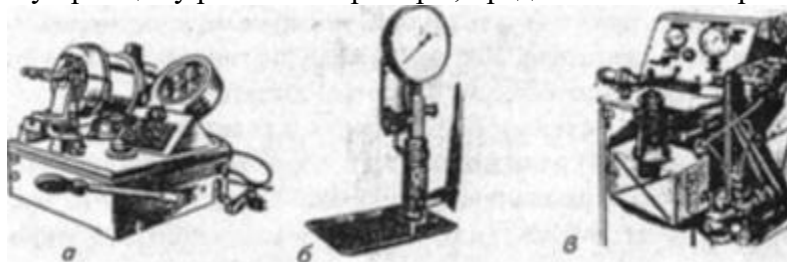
Приборы для испытания и регулировки форсунок: а -- КИ-3333А; б -- КИ-562; в -- КИ-1404
